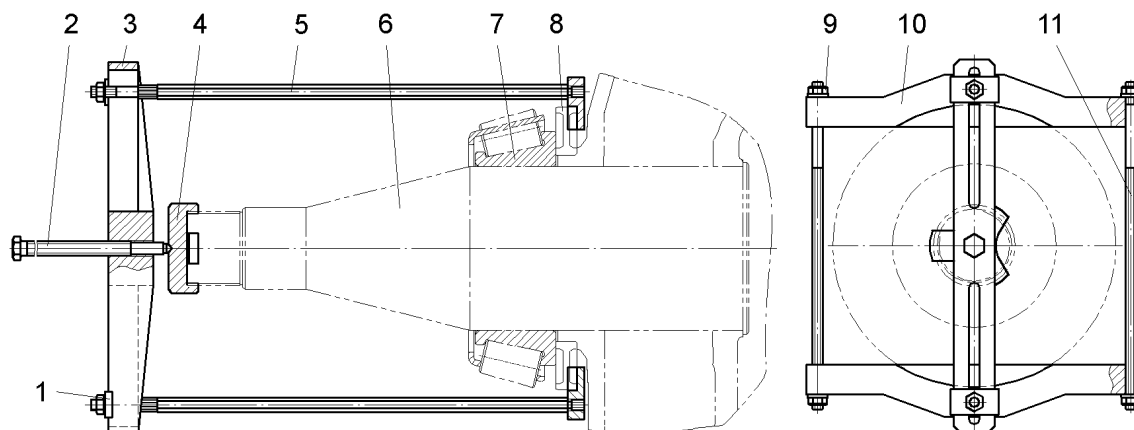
Приспособление для снятия внутреннего кольца внутреннего подшипника вместе с крышкой:
